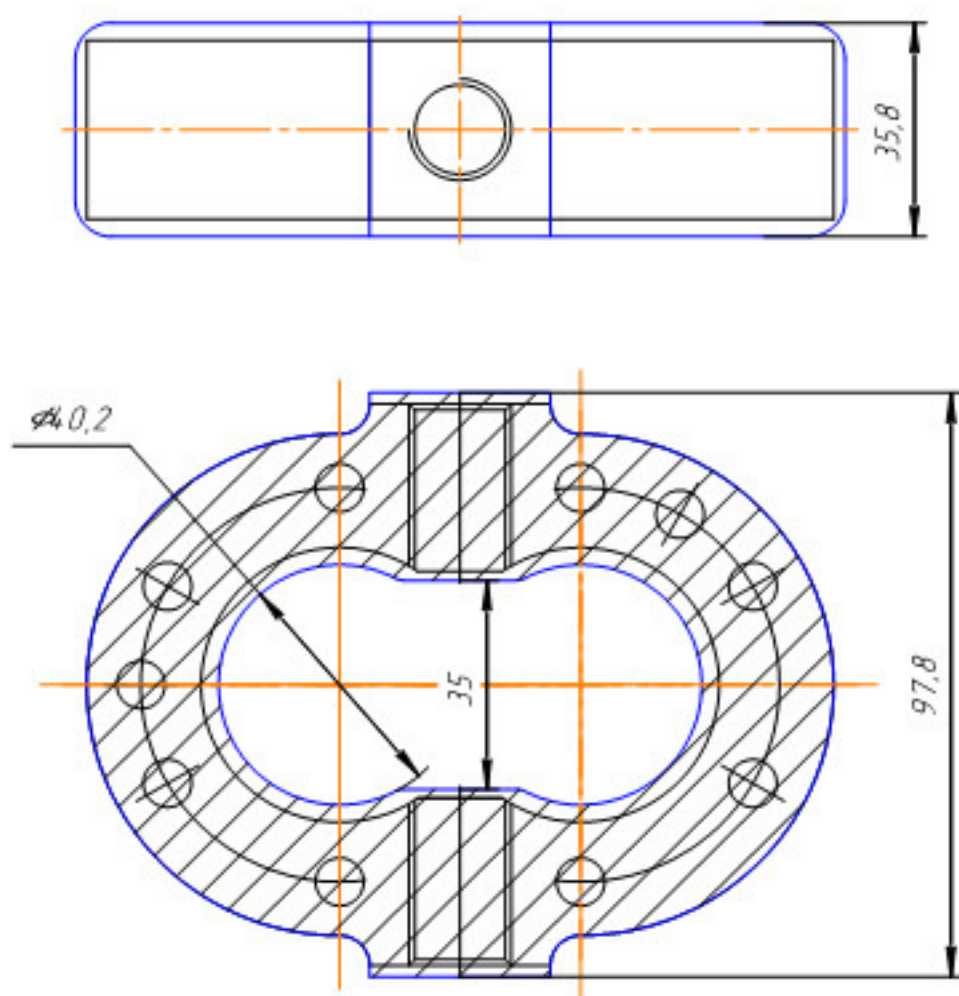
Ескіз заготовки при литті в облицьований кокіль
